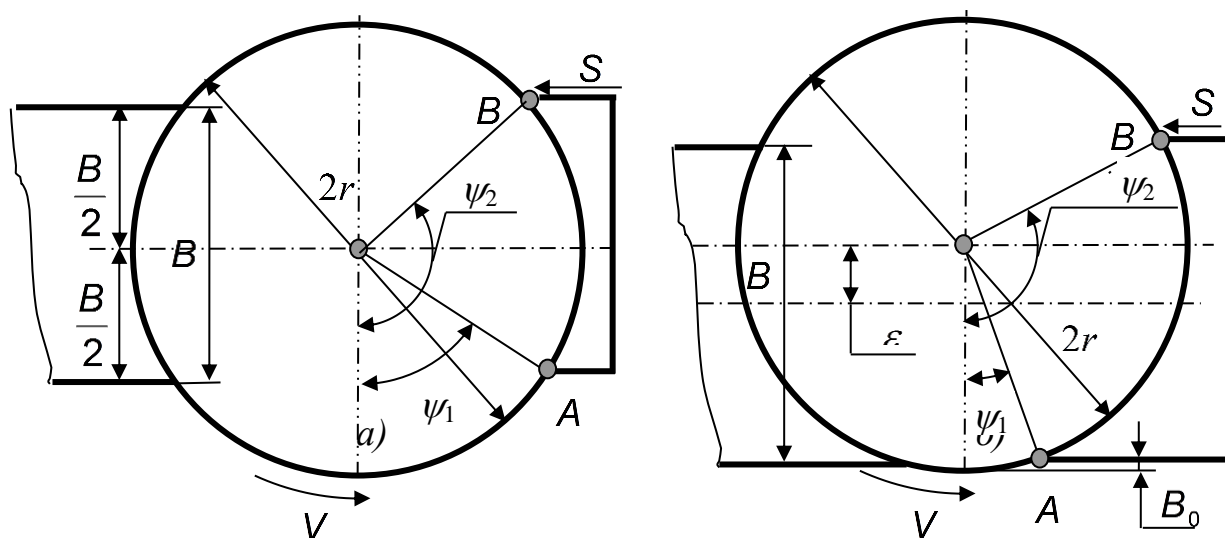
Схема розміщення фрези відносно заготовки:
